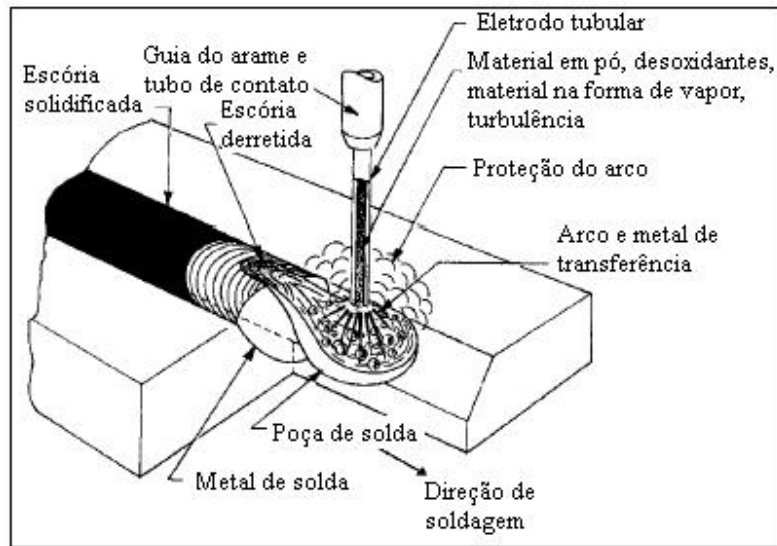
Soldagem com Eletrodo Tubular autoprotetido.
